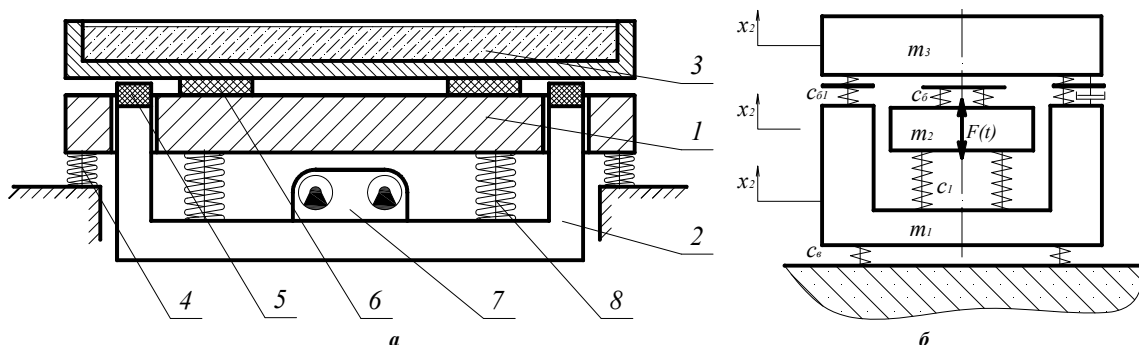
Віброударний майданчик: а) конструктивна схема; б) розрахункова схема
